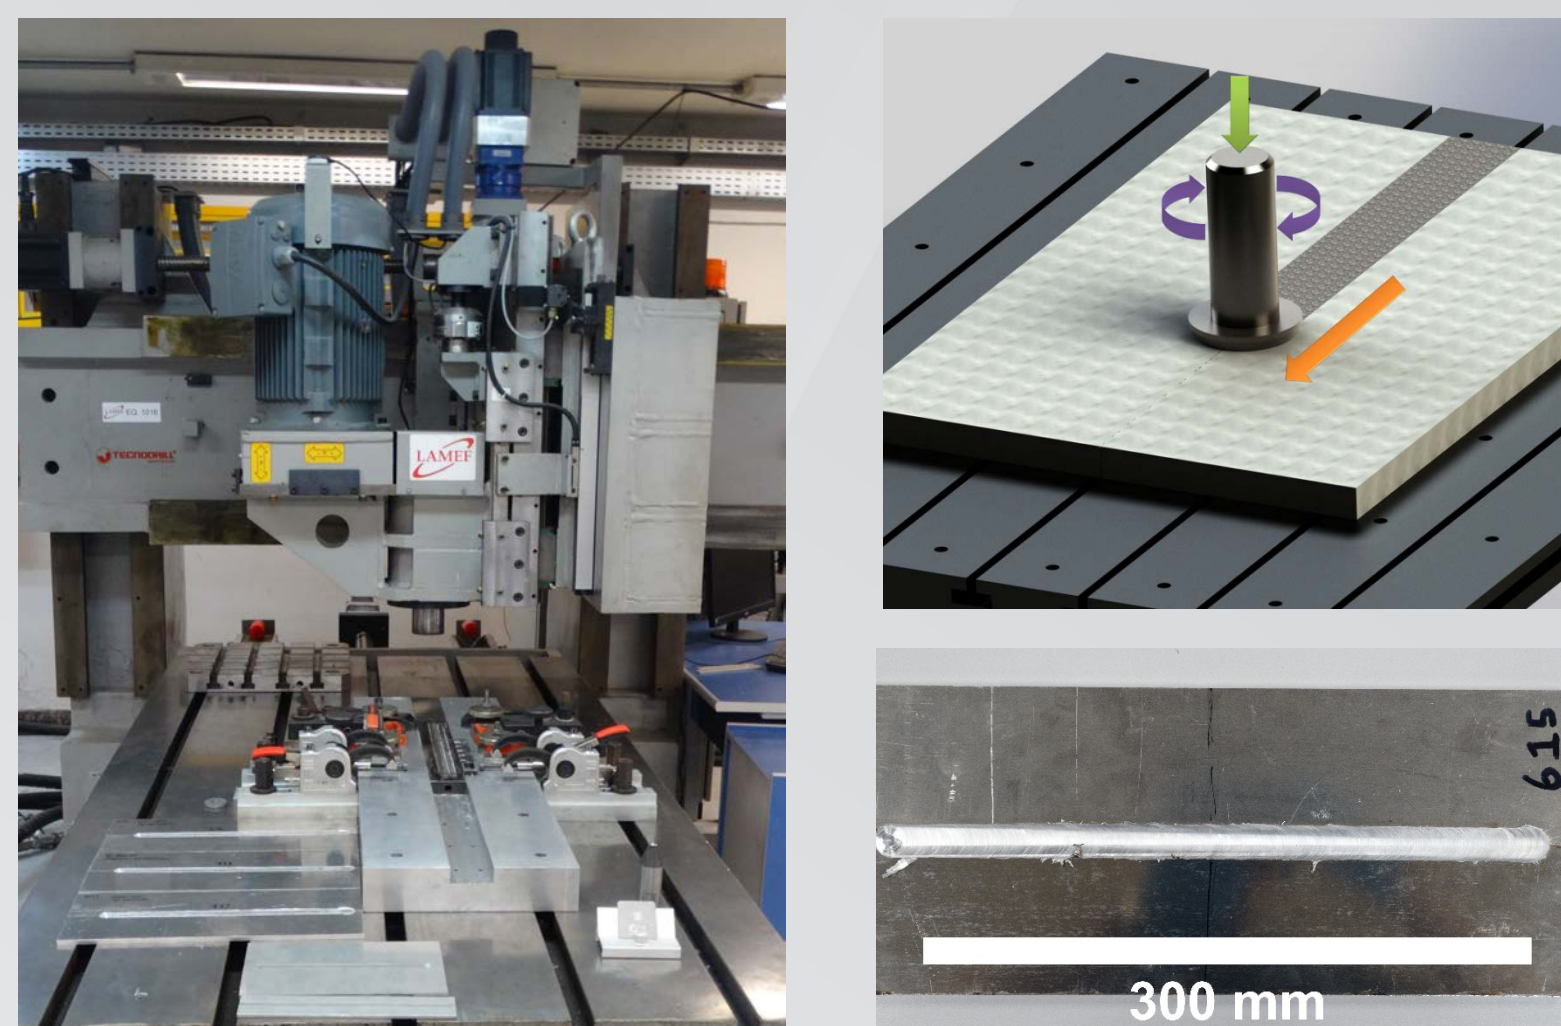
Processo de soldagem por fricção e mistura mecânica / região de solda entre duas chapas
